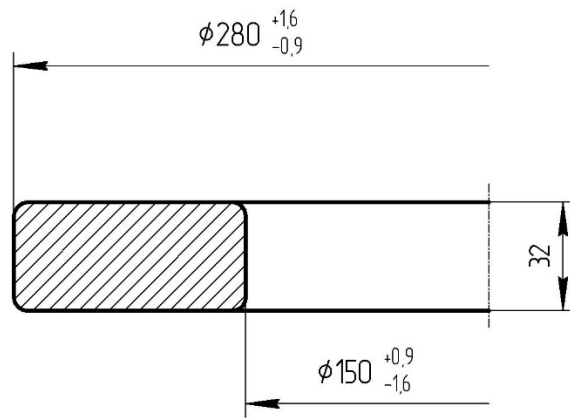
Ескіз заготовки після вільної ковки на молотах
